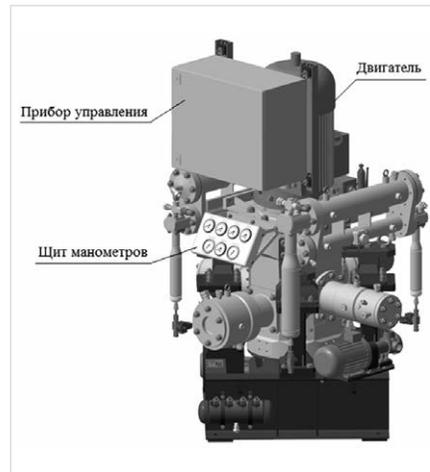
3D модель 4 рядного электрокомпрессора с вертикальным валом
